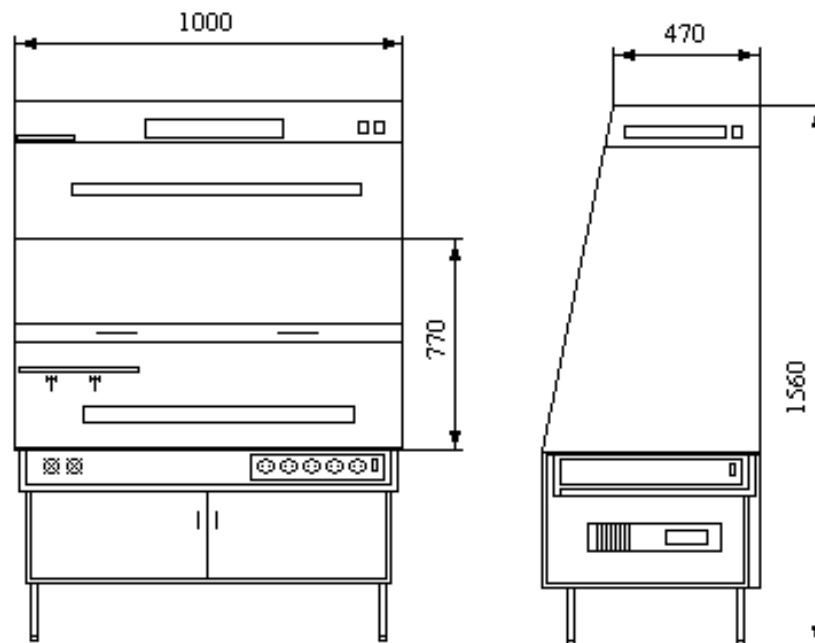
Витяжна шафа для виготовлення печатних плат
